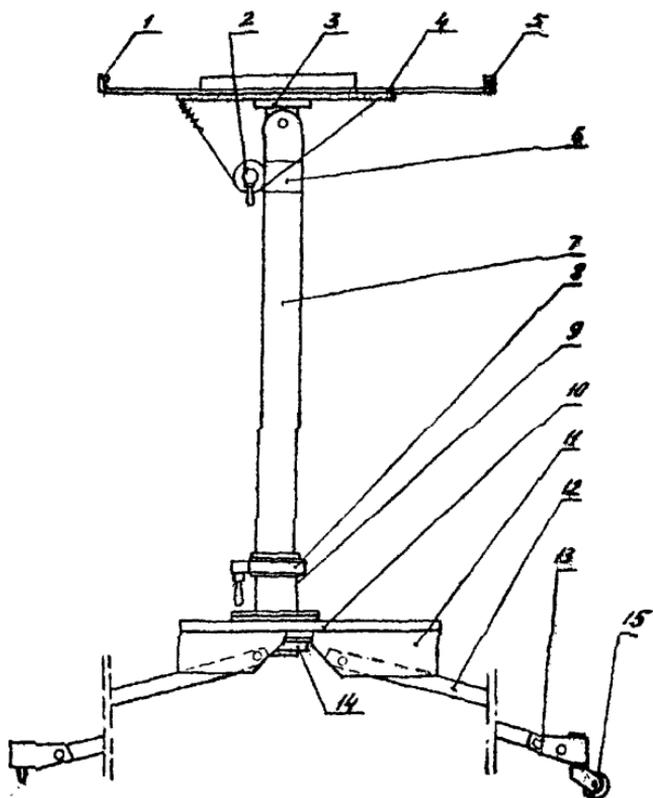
Штатив для установки дефектоскопов: 1, 5 - упор; 2 - фиксатор; 3 - стойка; 4, 10 - основание; 6, 8 - коугт; 7 - труба; 9 - каретка; 11 - sleeve (алюминий); 12 - нога; 13 - опора; 14 - гайка; 15 - ролик.
